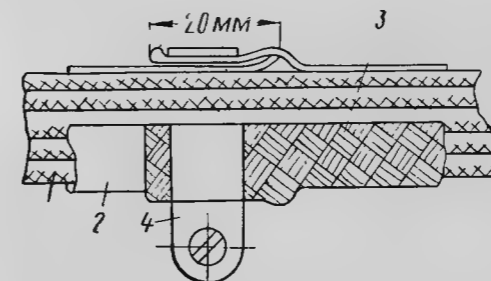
Стык экранирующей плетенки с трубопроводом:
